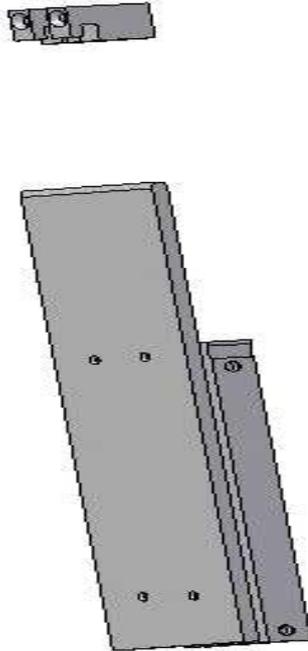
Vista del disegno iniziale del gruppo di contrasto frontale in cui è presente la slitta Gimatic, la piastra frontale di fermo e il fine corsa superiore
